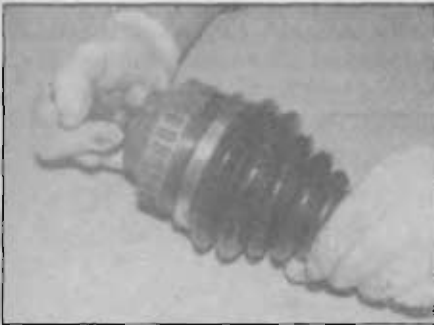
Надвиньте защитный чехол на корпус ШРУСа и расположите его в канавке корпуса ШРУСа
